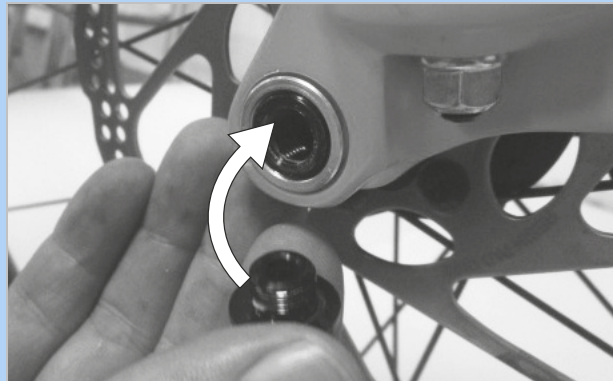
Wsunąć oś zgodnie z kierunkiem strzałki
